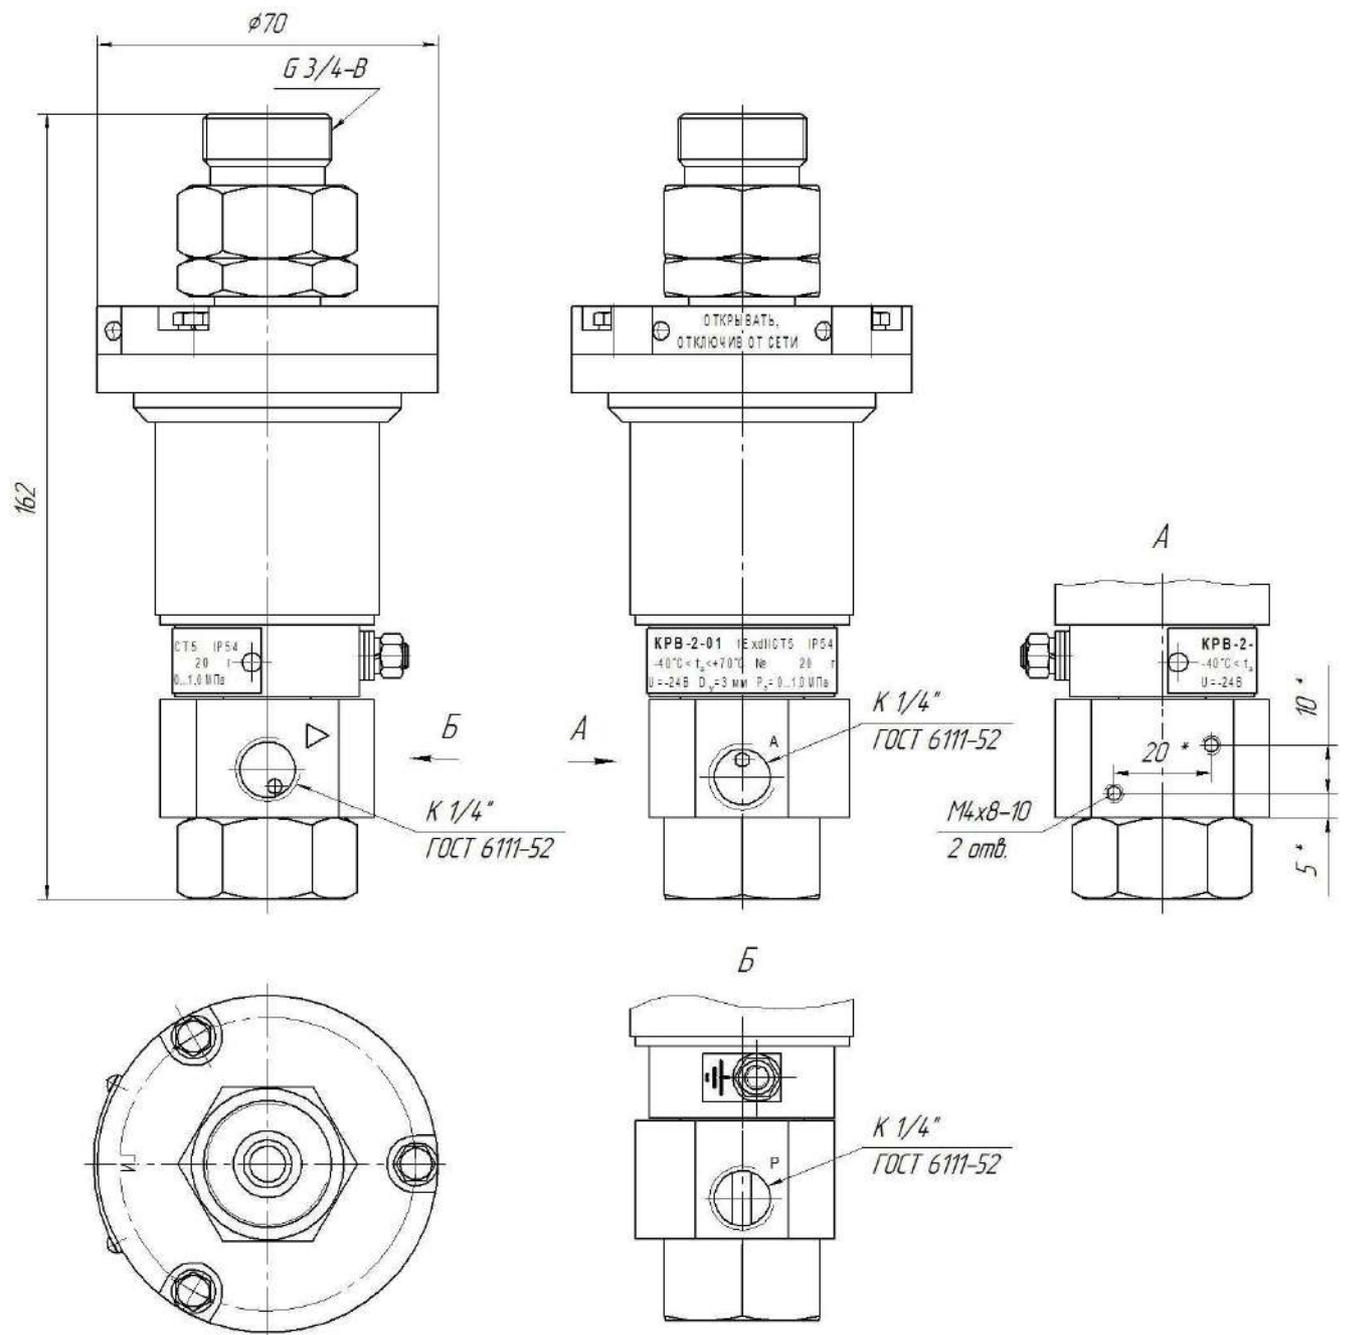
Габаритные и присоединительные размеры клапана КРВ-2
